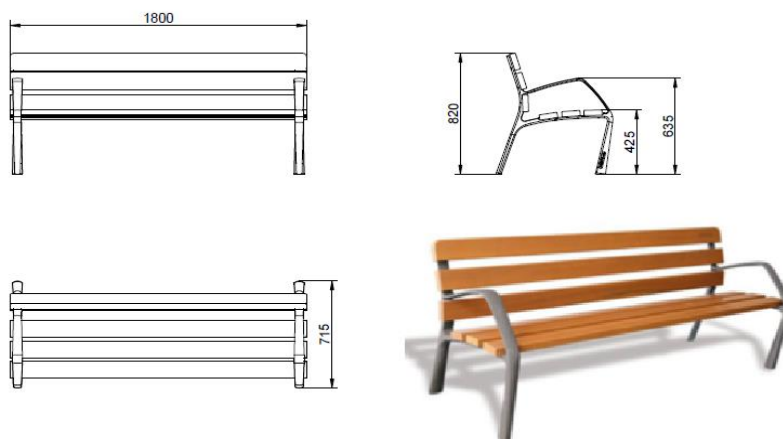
Croquis sin escala e imagen del banco escogido. (Fuente: www.glsprefabricados.com)
